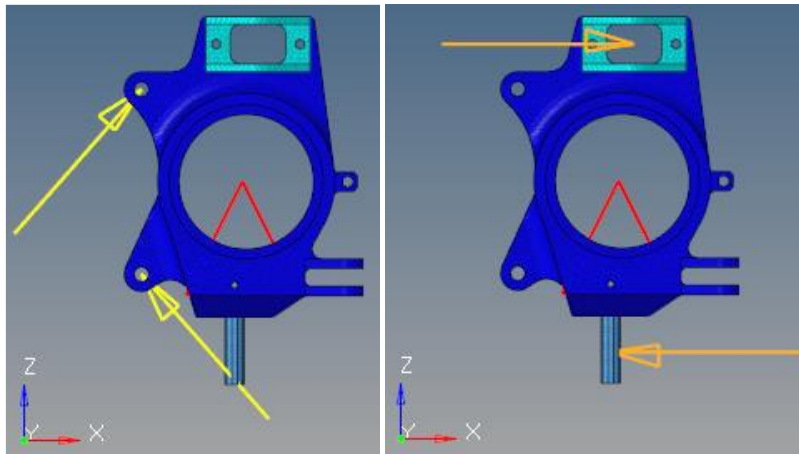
a) Fuerza aplicada sobre el soporte del caliper en el caso de frenado crítico.
